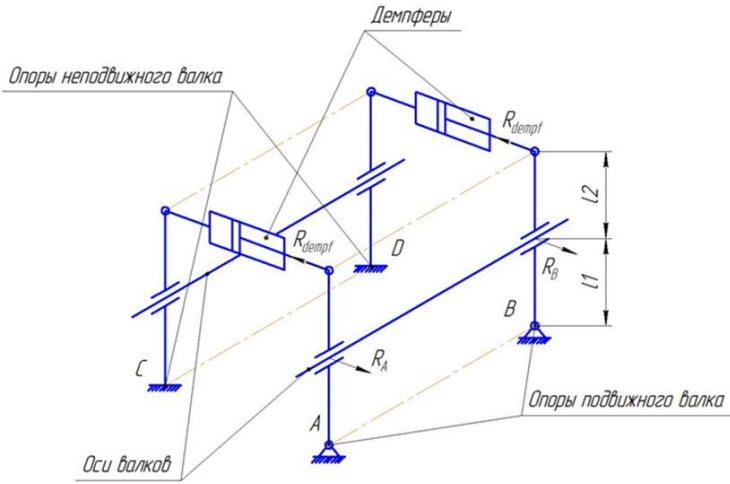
Схема расположения демпферов предохранительного устройства для защиты валкового пресса от перегрузок
